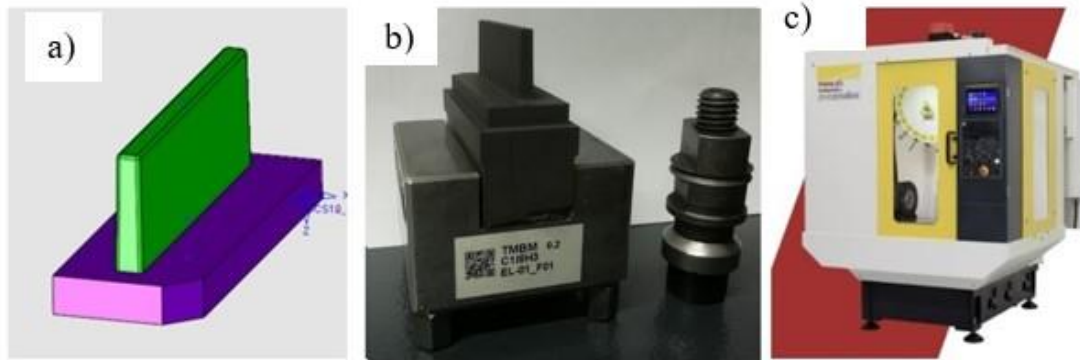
a) CAD do Eléctrodo-Rib; b) Eléctrodo-rib; c) Centro de maquinagem CNC Fanuc
